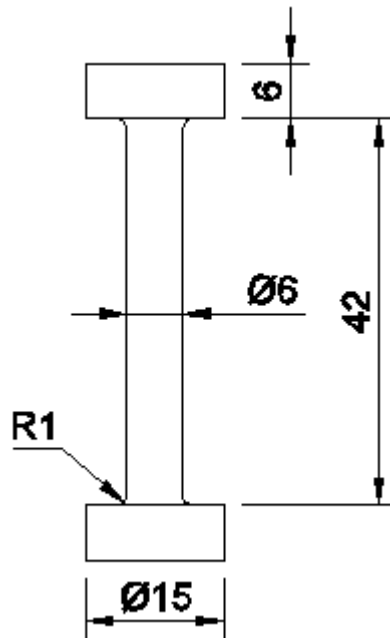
Dimensões em mm do corpo de prova para ensaio mecânicos.
